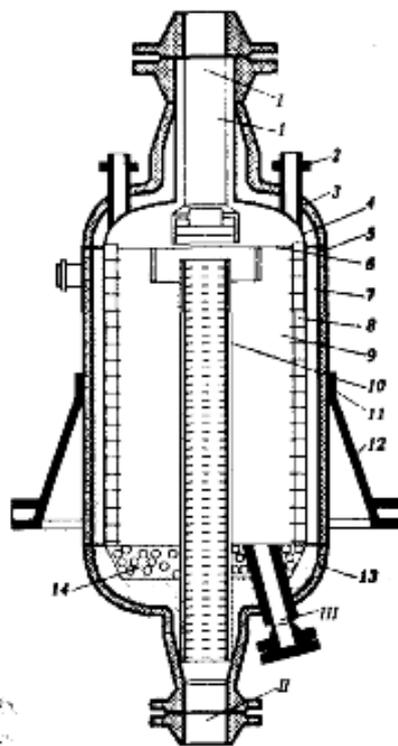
Реактор риформинга: 1- распределитель; 2 - штуцер для термопары; 3 - днище верхнее; 4 - кожух; 5 - корпус; 6 - тарелка; 7 - футеровка; 8 - желоб; 9 - катализатор; 10 - труба центральная; 11 - пояс опорный; 12 - опора; 13 - днище нижнее; 14 - шары фарфоровые; I - ввод сырья; II - вывод продукта; III - вывод катализатора
